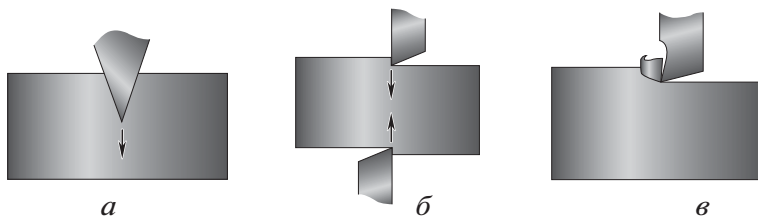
Виды резания металла: *а* — с помощью клинообразного инструмента; *б* — с помощью двух режущих лезвий; *в* — снятие стружки
